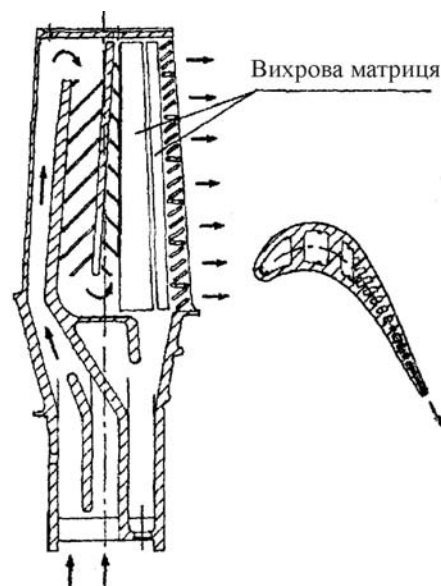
Конструкція охолоджуваної робочої лопатки з вихровою матрицею
